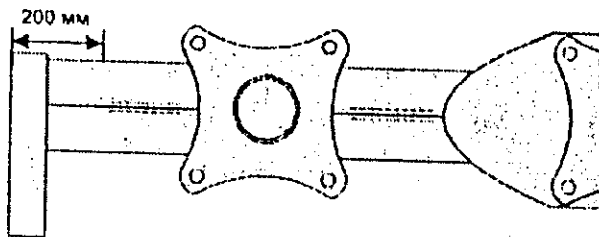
Контроль сварного шва нижней стенки продольной балки рамы
